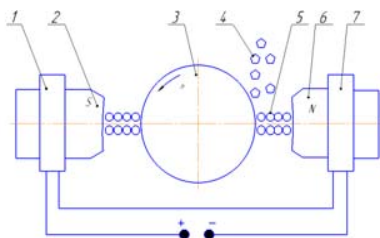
Схема магнитно-абразивной обработки наружных поверхностей: где 1 и 7 – магнитопроводы электромагнитной системы; 2 и 6 – полюса; 3 – обрабатываемая деталь; 4 – подаваемый ферроабразивный порошок; 5 – цепочки ферроабразивного порошка
